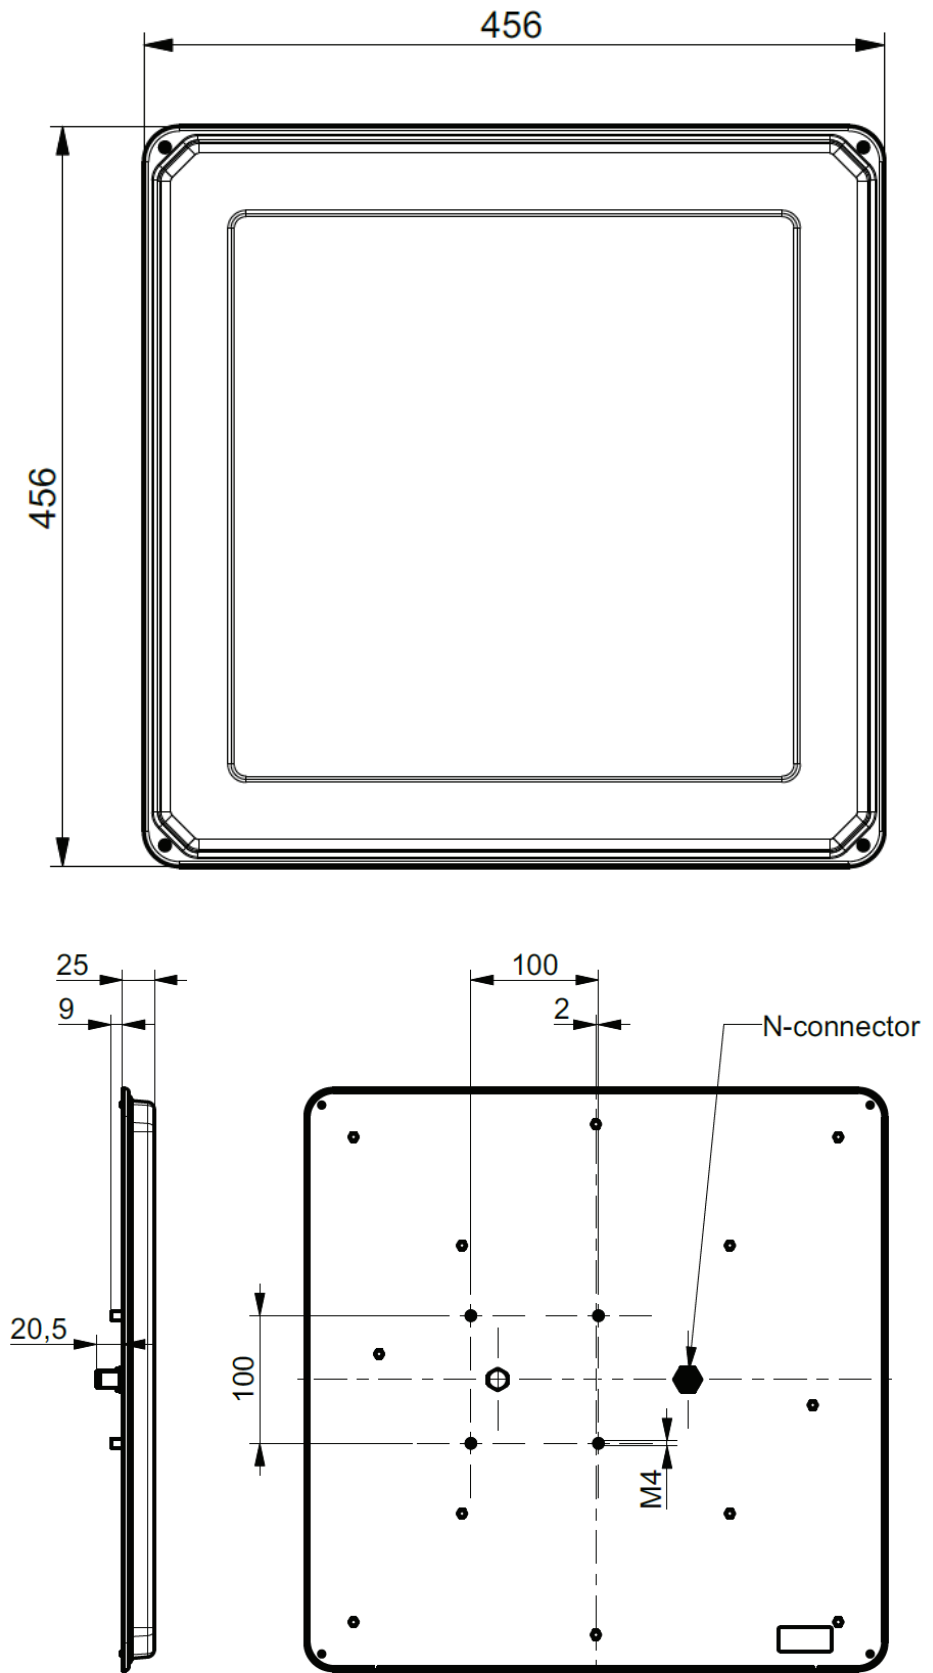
Abmessungen für WiRa 40° (52010251, -252)
